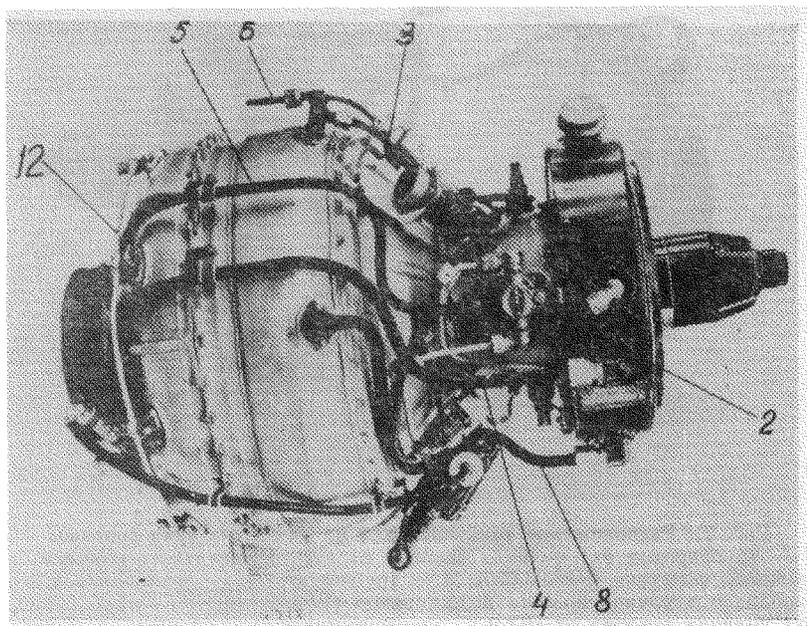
Расположение трубопроводов на двигателе (вид сверху):
